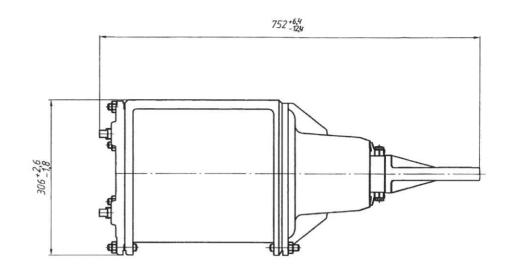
Общий вид тормозного цилиндра 710-03
